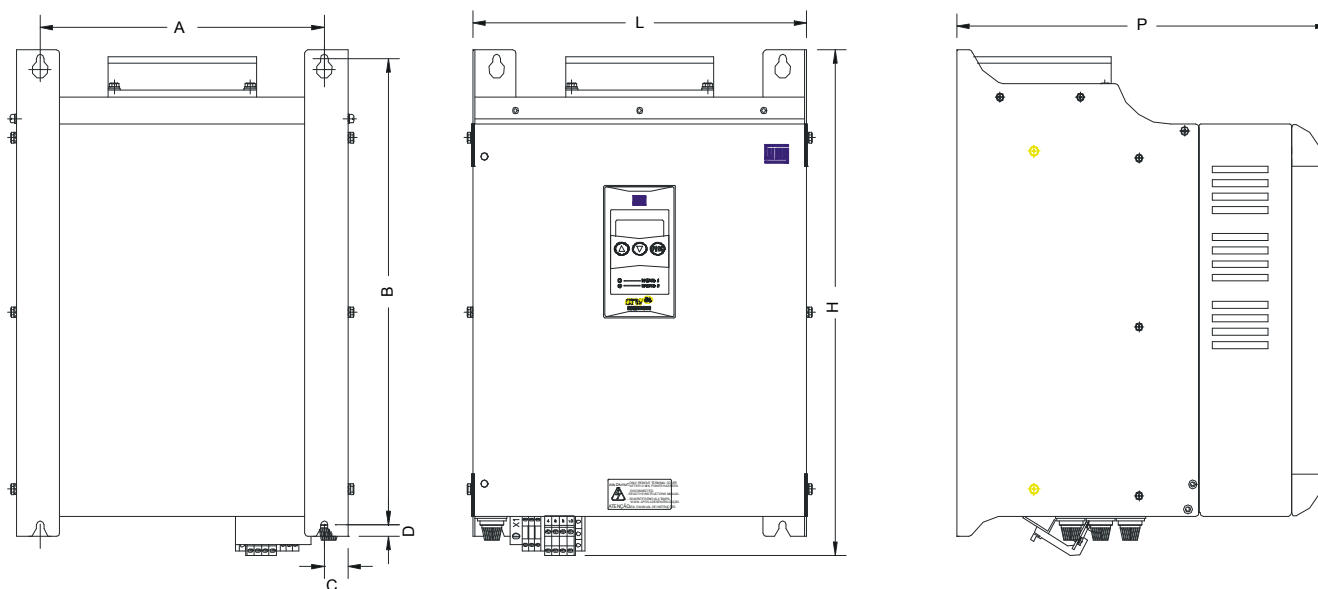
b) – Dimensional do Conversor CTW-04 - Mec 02
